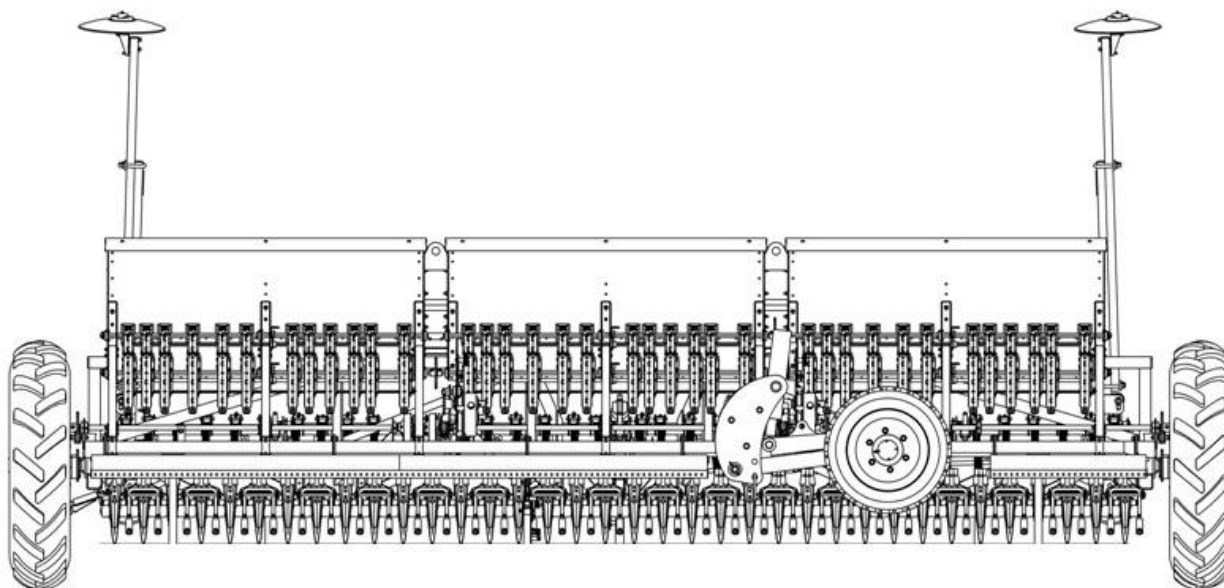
Общий вид сеялки с установленной траверсой и опорными колесами.
